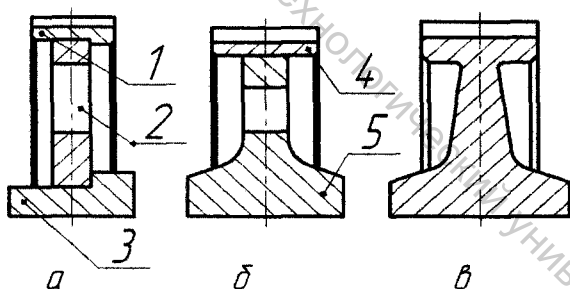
Конструктивные варианты заготовки шестерни:
